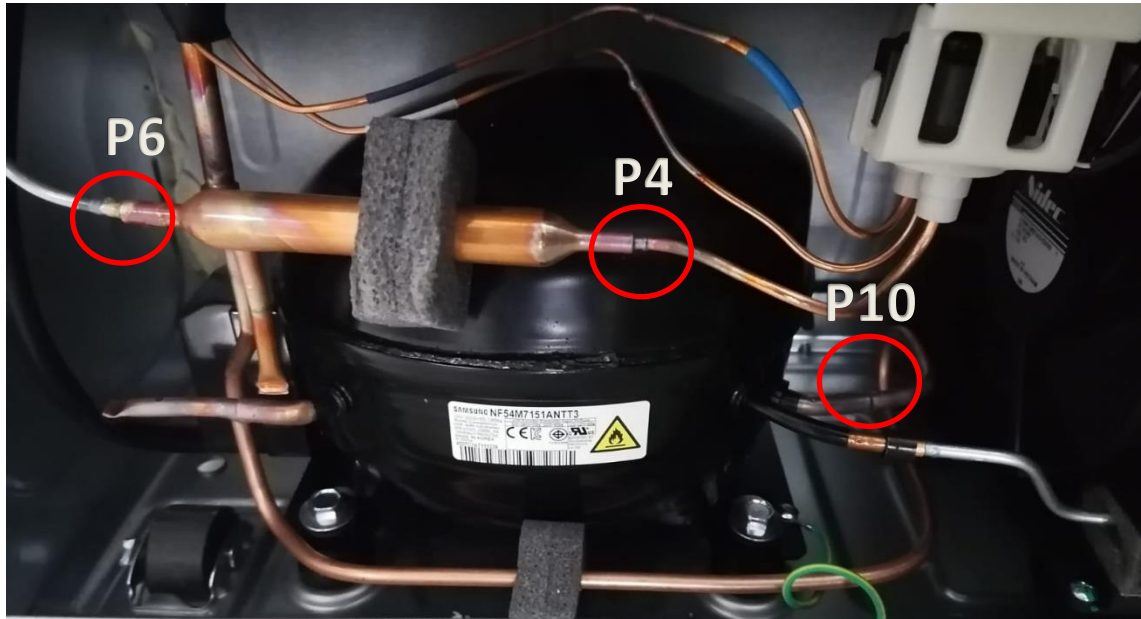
Ubicación de los puntos de soldadura p10, p6 y p4.
